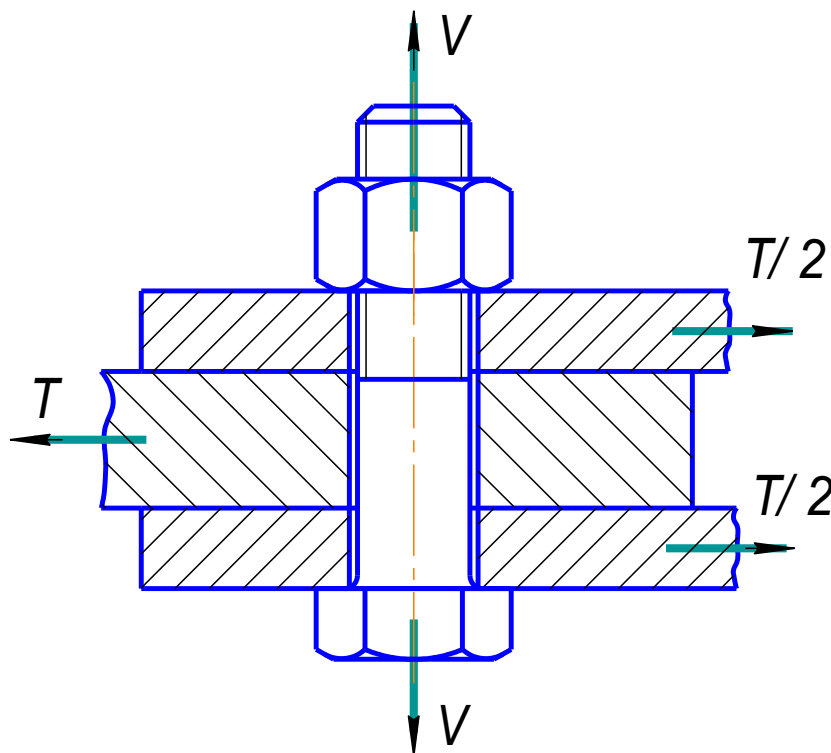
Схема для розрахунку болтового з'єднання, навантаженого поперечною силою
